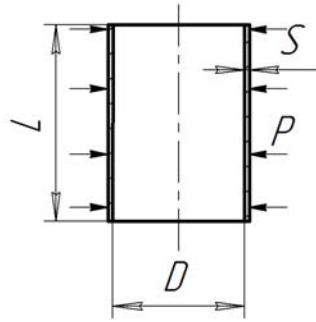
Розрахункова схема циліндричної обичайки, навантаженої зовнішнім тиском.
